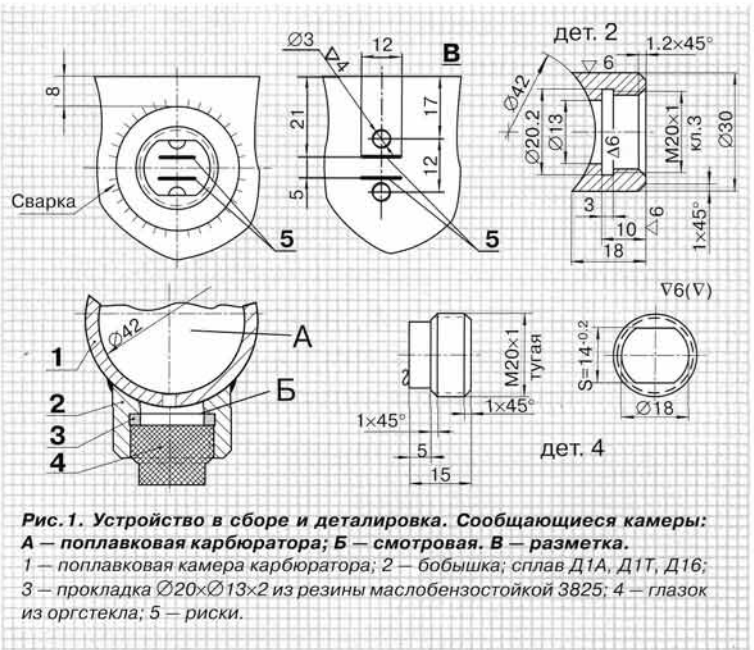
Устройство в сборе и детализовка. Сообщающиеся камеры: А — поплавковая карбюратора; Б — смотровая. В — разметка. 1 — поплавковая камера карбюратора; 2 — бобышка; слав Д1А, Д1Т, Д16; 3 — прокладка Ø20×Ø13×2 из резины маслбензостойкой 3825; 4 — глазок из оргстекла; 5 — риски.
